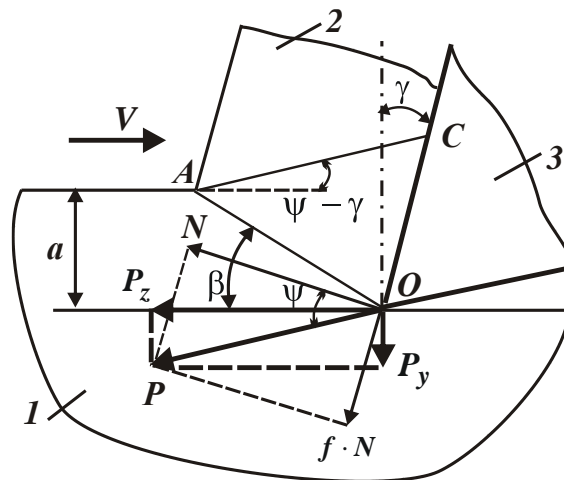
Розрахункова схема параметрів стружкоутворення під час процесу різання: 1 – оброблюваний матеріал; 2 – стружка, що утворюється; 3 – ріжучий інструмент
